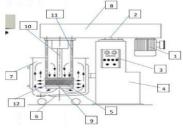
Prinsip Kerja Mesin *Basket Mill* (Sumber : iyltmy.co.id)
